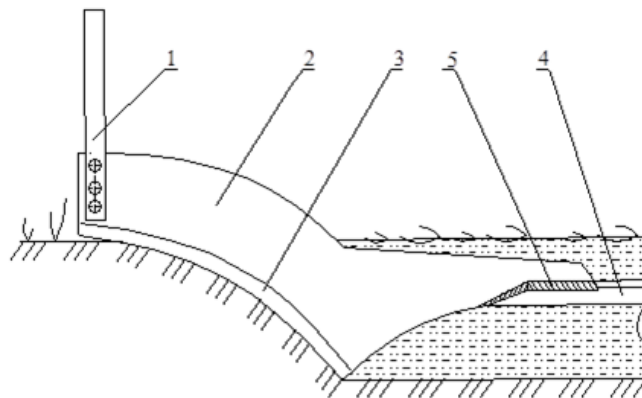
Схема робочого органу культиватора для підвищення якості обробітку: 1 – стійка; 2 – пластина; 3 – ріжуча кромка пластини; 4 – підрізаючі елементи; 5 – косинка.
